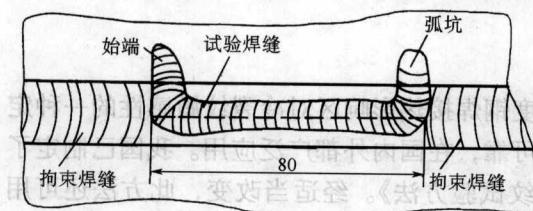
焊条电弧焊的试验焊缝^[1]
